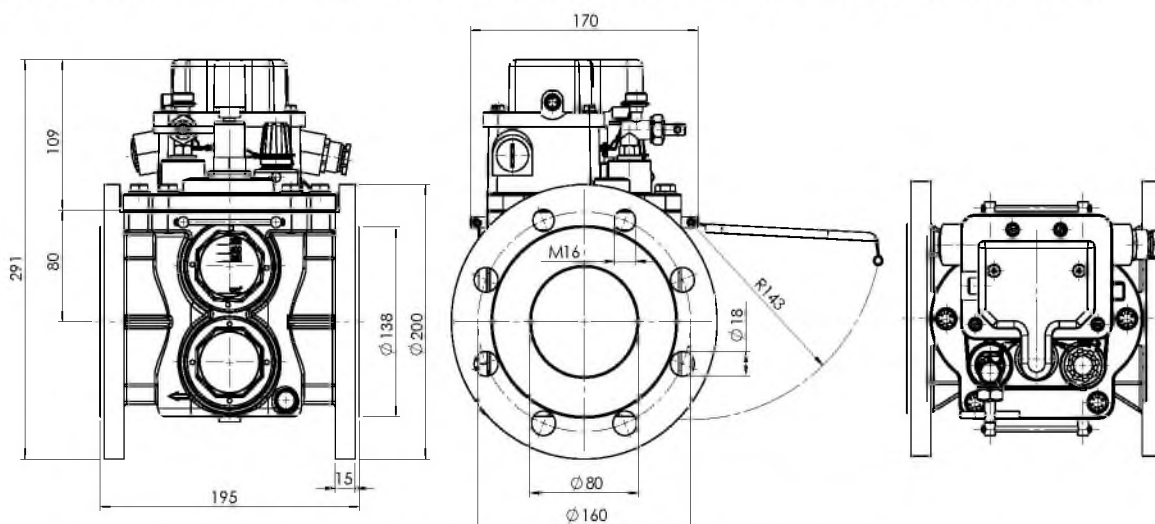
Размерный эскиз газового реле типорядаNM типа 26 (BF 80/10/8)
